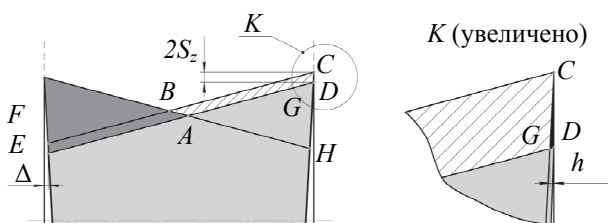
Схема формирования пропила дисковой твердосплавной пилой с попеременно-косым профилем зубьев
